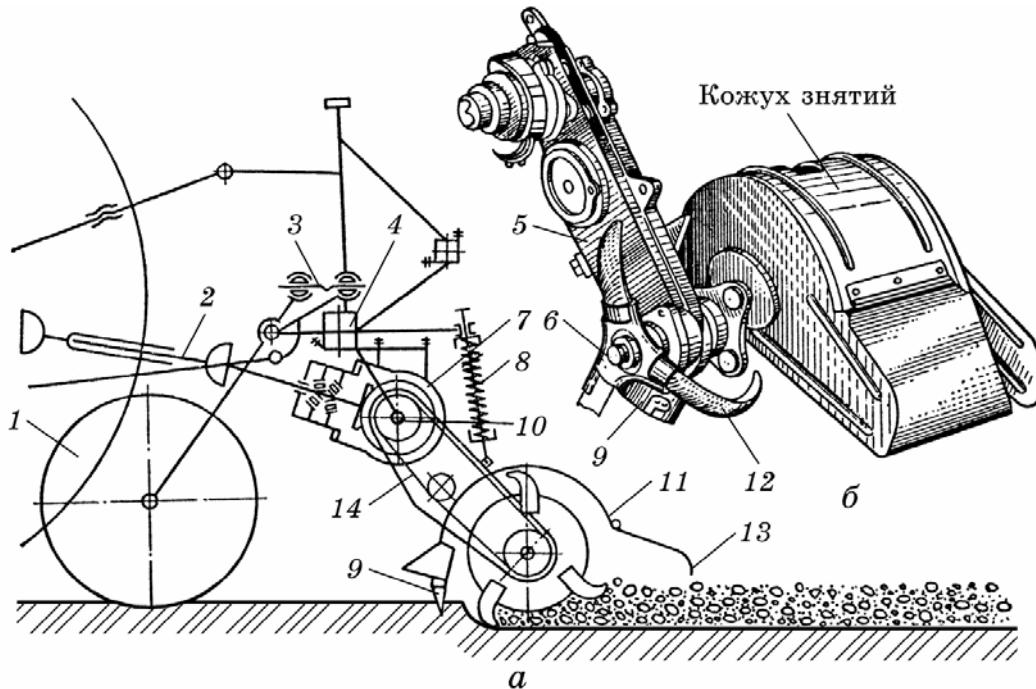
Культиватор фрезерний КФ-5,4: а – принципова схема; б – робоча секція; 1 – опорне колесо; 2 – карданна передача; 3 – гвинтовий механізм; 4 – рама; 5 – корпус; 6 – диск; 7 – редуктор; 8 – штанга з пружиною; 9 – пасивний ніж; 10 – вал; 11 – кожух; 12 – активний ніж; 13 – фартух; 14 – ланцюгова передача
